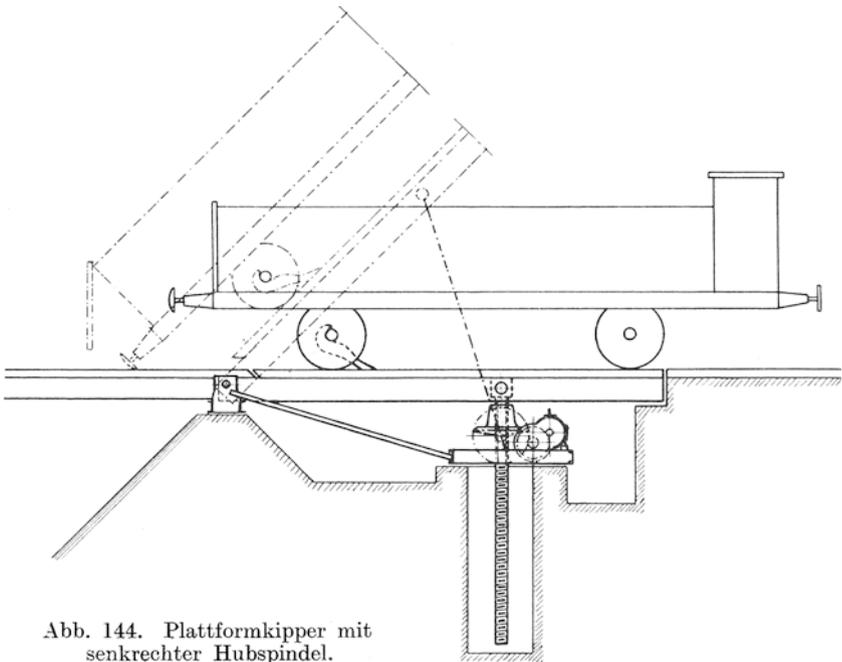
Plattformkipper mit senkrechter Hubspindel.
